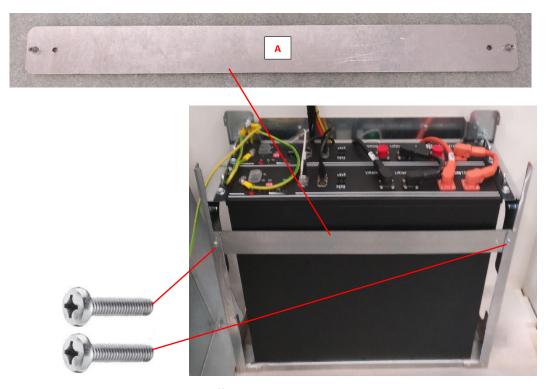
Installazione staffa segregazione batterie sul WALL-BOX-Bx BASE
